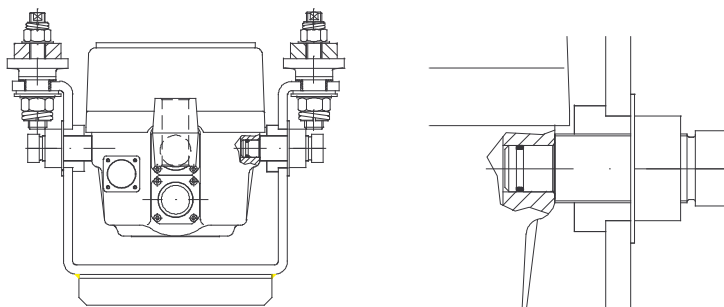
Sezione trasversale in corrispondenza del collegamento cassa-traversa: vista d'insieme (a sinistra), particolare (a destra)
